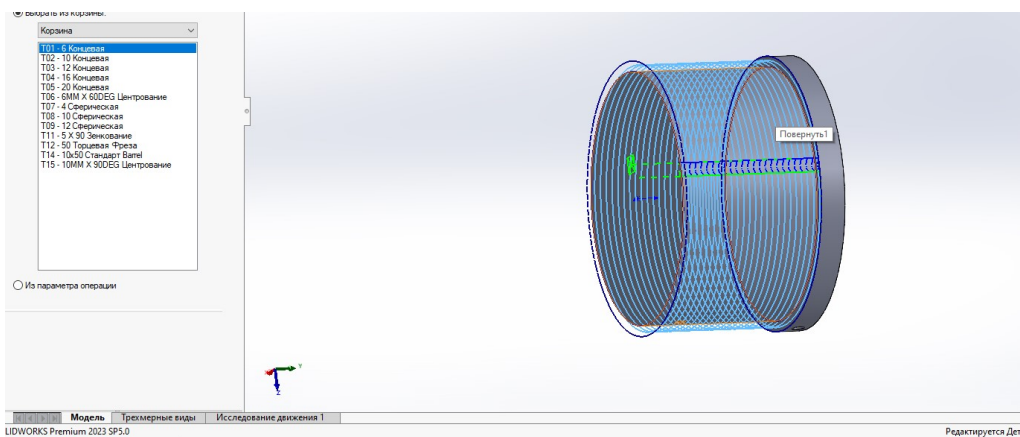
Траєкторія вершини ріжучого інструменту
